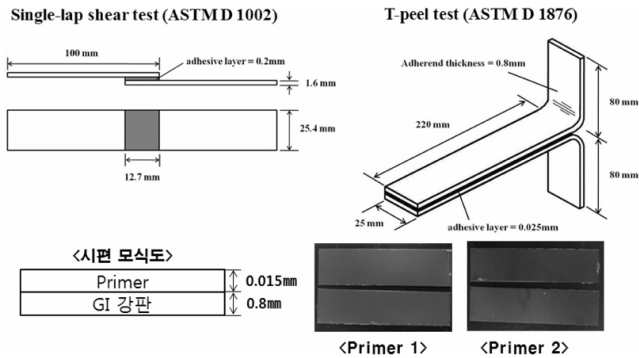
자동차용 pre-primed 도료의 비용접식 접합강도 측정을 위한 Single-lap shear test와 T-peel test 규격.
